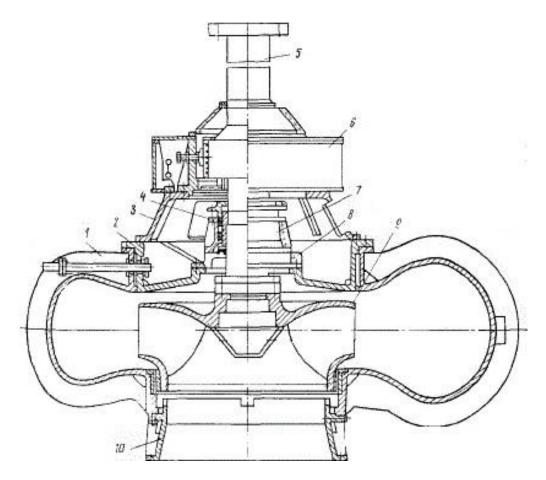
Вертикальный насос: 1 — корпус; 2 — верхняя крышка корпуса; 3 — ребра жесткости; 4 — торцевое уплотнение; 5 — вал; 6 — кожух; 7 — направляющий подшипник; 8 — фланец вала; 9 — рабочее колесо; 10 — всасывающий патрубок
